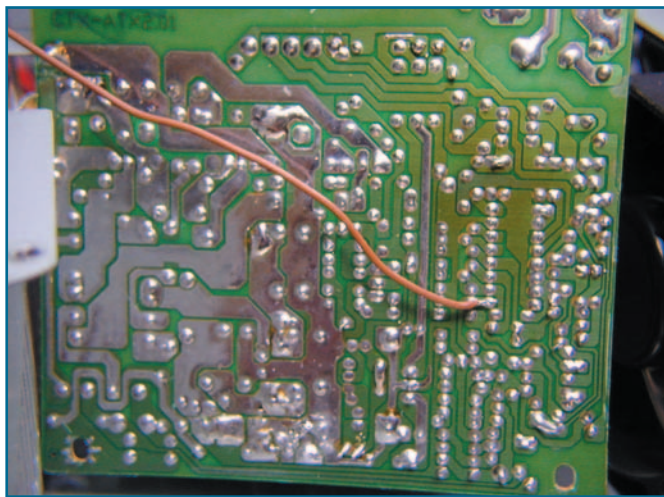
Cable soldado a patilla nº1 del TL494.
